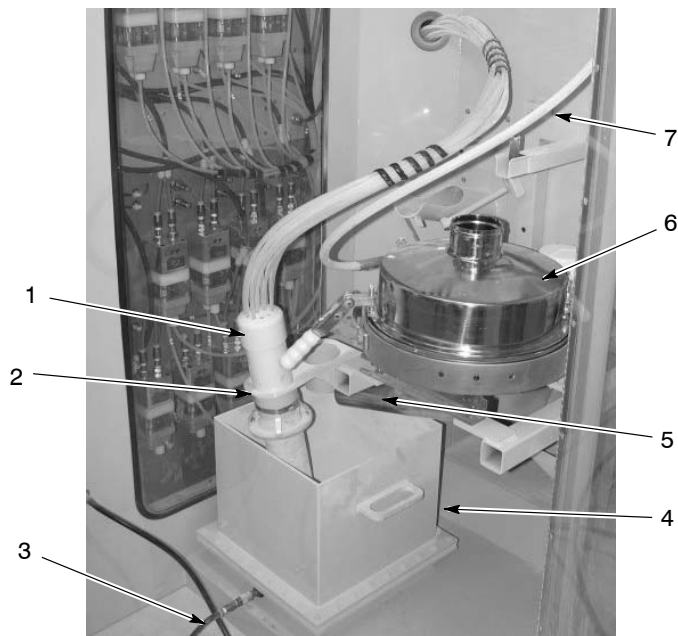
Установка и соединения бункерного питателя и просеивателя
